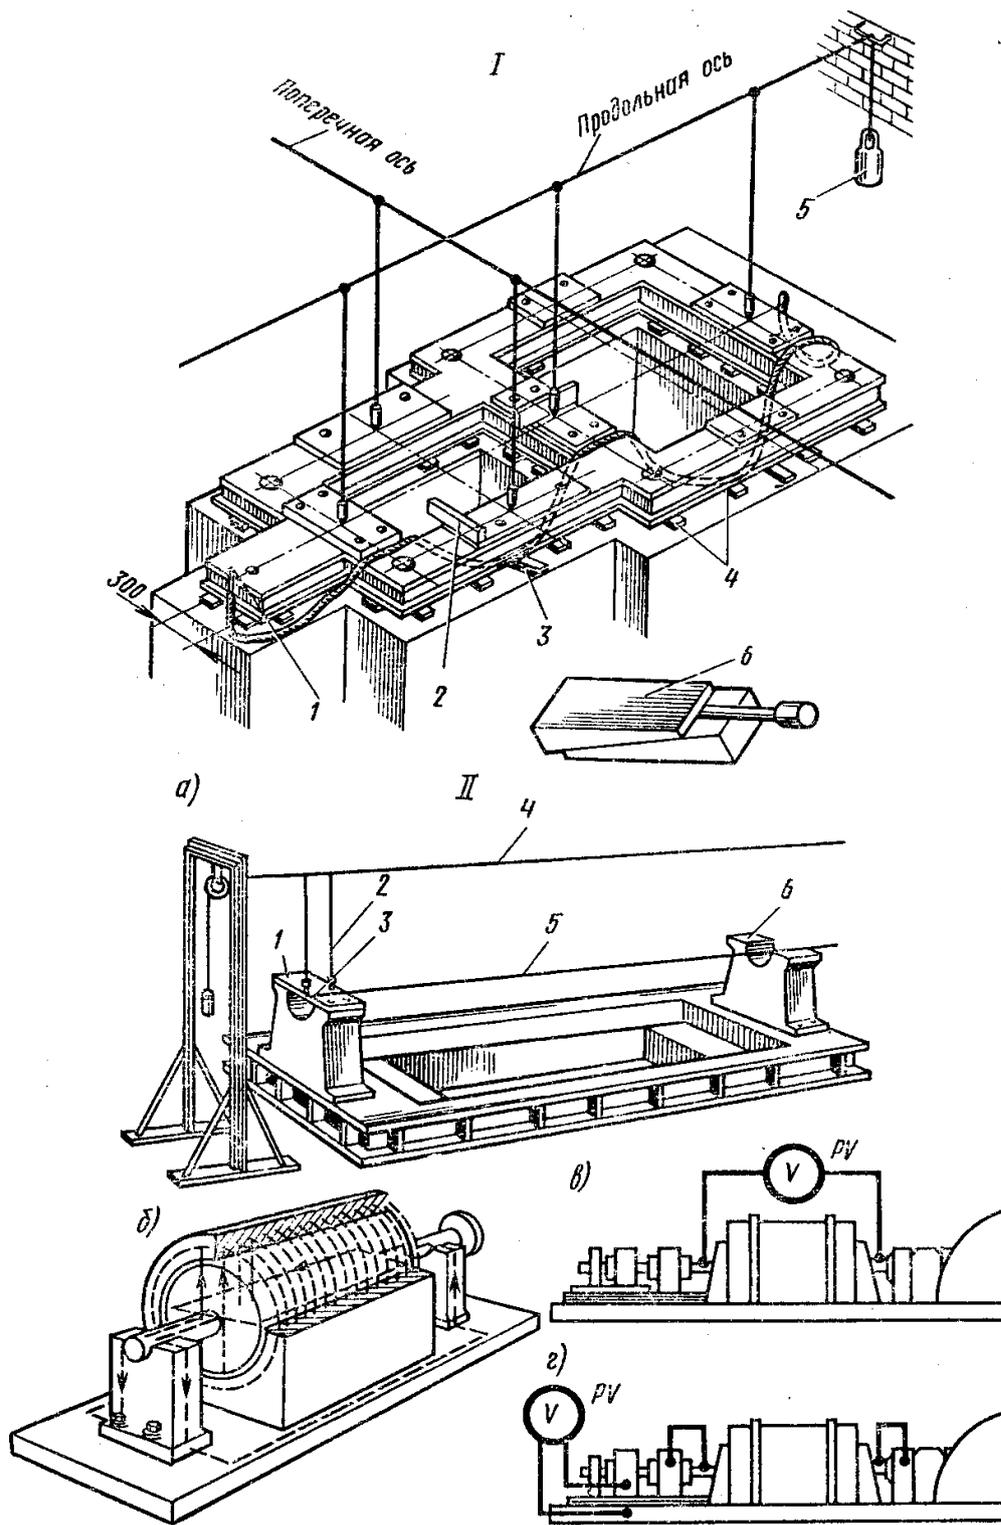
Фундаментная плита и схема установки и проверки изоляции подшипниковых стояков: I - установка фундаментной плиты: 1 - гидростатический уровень; 2 - уровень; 3 - стальной клин; 4 - прокладка; 5 - груз; 6 - клиновый домкрат; II - установка подшипниковых стояков (а) и проверка изоляции; 1 - пластина; 2 - отвес; 3 - риска; 4 - монтажная струна; 5 - контрольная струна; 6 - стояк; б, з - схема прохождения тока через подшипник; в, г - проверка изоляции стояка подшипника проверочных линеек, уложенных на опорные плоскости.
